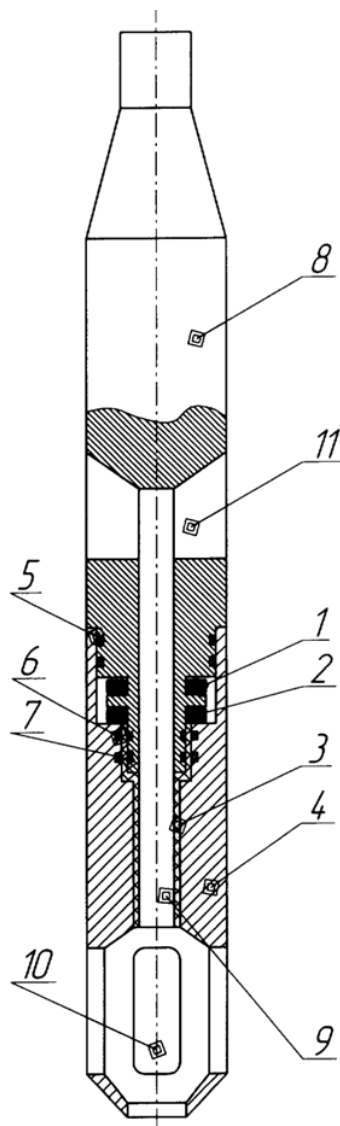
Схематический вид прибора индукционной резистивиметрии РИС-42. 1 – генераторная катушка; 2 – измерительная катушка; 3 - диэлектрической втулки; 4 – корпус 5, 6, 7, 8 - уплотнительных элементов (герметизирующих резиновых колец); 9 – отверстие для свободно заполняющей жидкости; 10 – заборник; 11 - полость для выхода скважинной жидкости;
